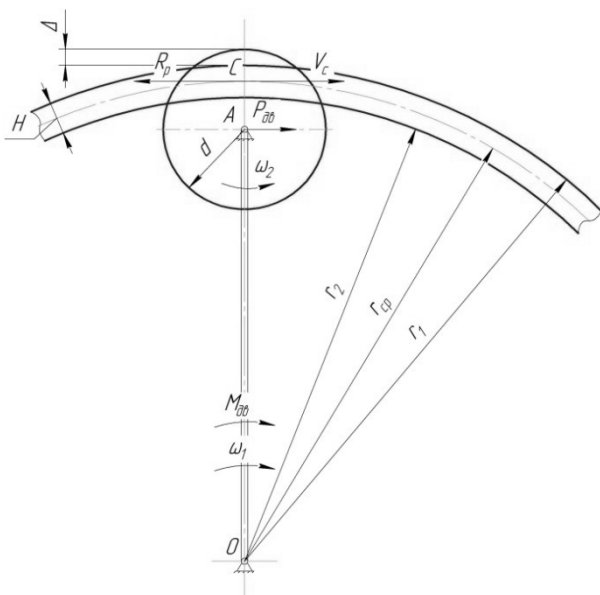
Кинематическая схема совокупности круговых движений инструментального блока и притирочных инструментов
